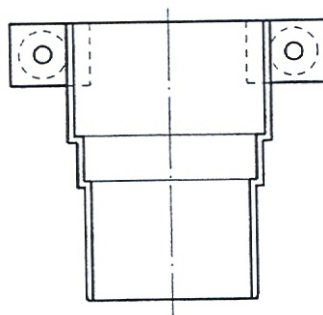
Exemplo de um acoplador de tubo com fixação e saída com terminal macho
